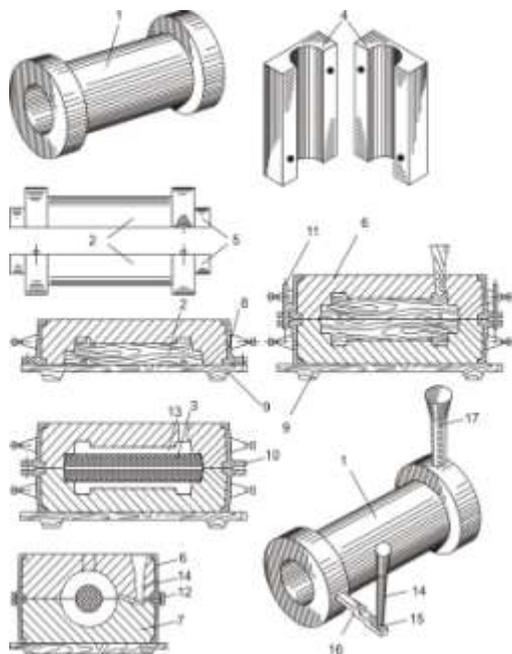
Последовательность изготовления чугунной отливки втулки: 1 – чертеж втулки; 2 – деревянная модель; 3 – стержень; 4 – стержневой ящик; 5 – стержневые знаки; 6 – верхняя полуформа; 7 – нижняя полуформа; 8 – опока; 9 – подопочный щиток; 10 – втулки; 11 – центрирующие штыри; 12 – скобы; 13 – полость формы; 14 – стояк; 15 – шлакоуловитель; 16 – питатель; 17 – выпор
